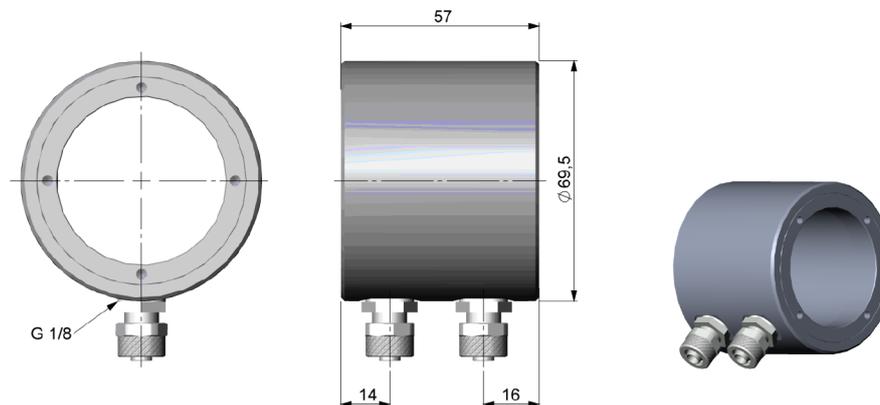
Abmessungen Wasserkühlgehäuse [TM-W-CTL], Schlauchanschluss: 6x8 mm, Gewinde (Fitting): G 1/8 Zoll
